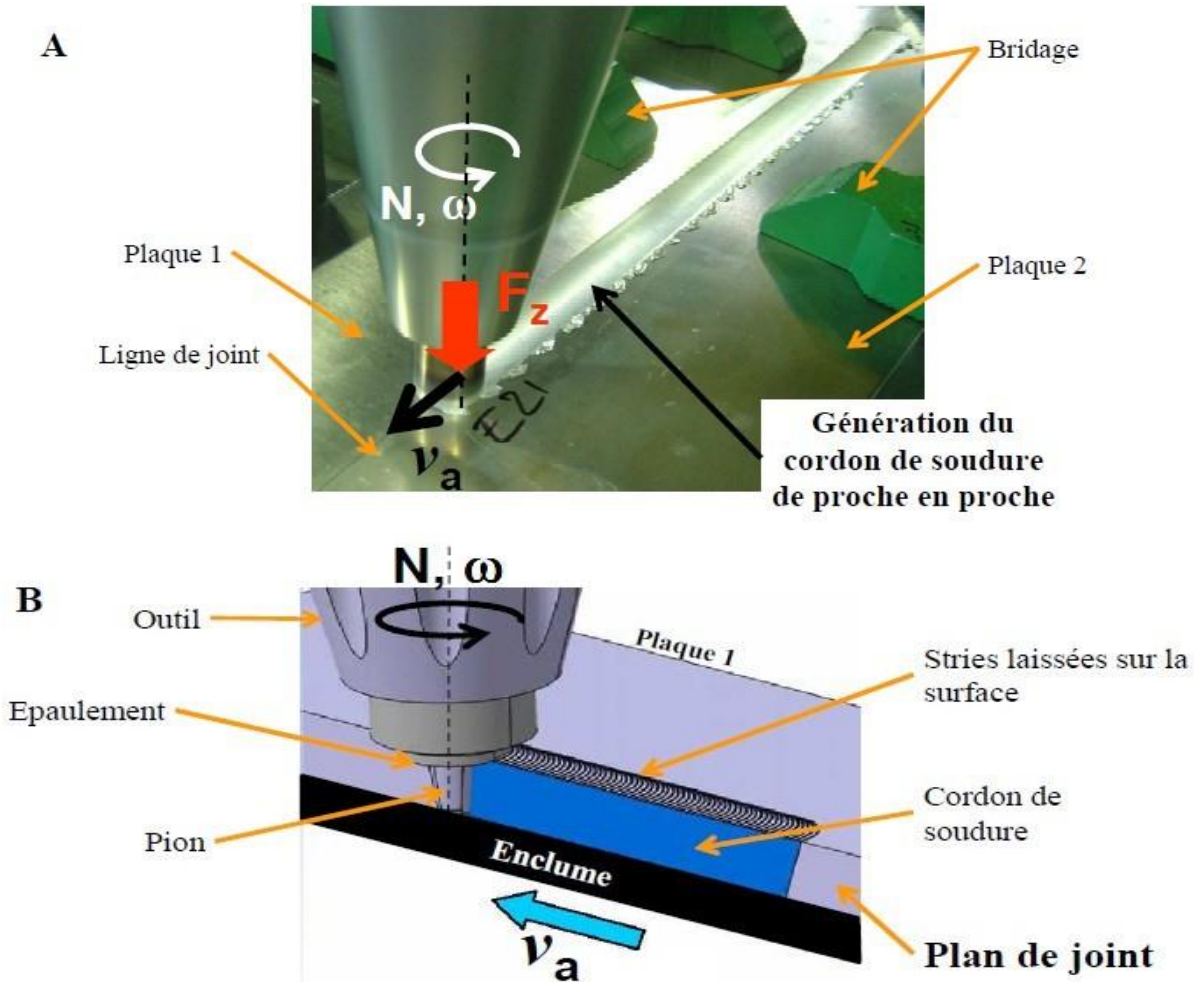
Présentation du soudage par friction malaxage. A-Soudure rectiligne de deux plaques mises bout about. B-Visualisation du plan de joint lors de la phase de soudure.
